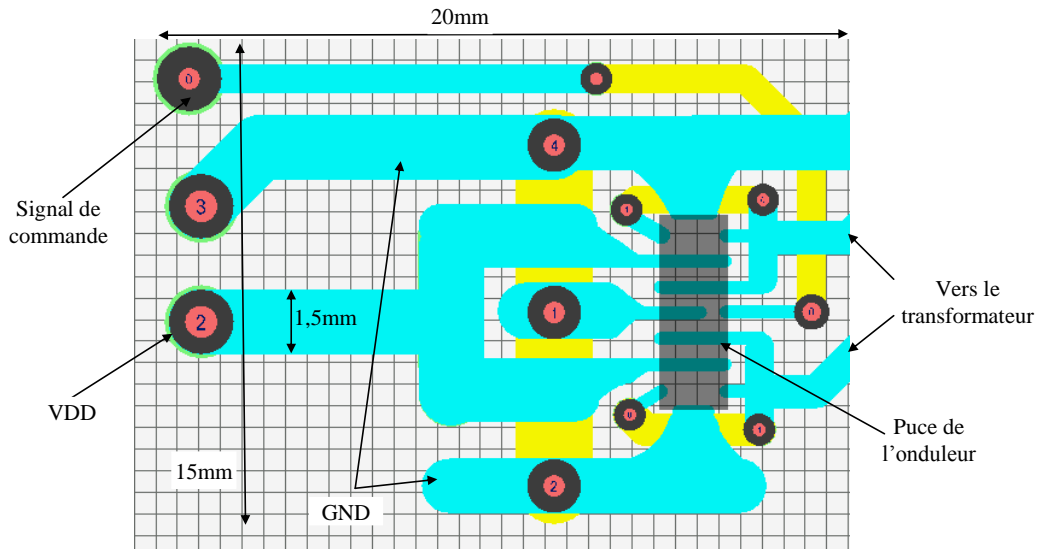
Dessin du PCB recevant les puces par flip-chip
